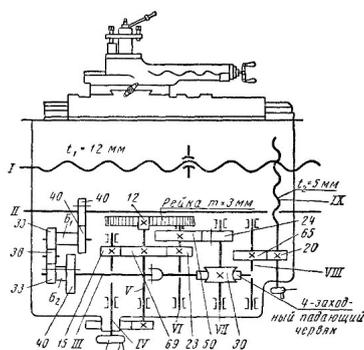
Кинематическая схема фартука токарно-винторезного станка 1А62
